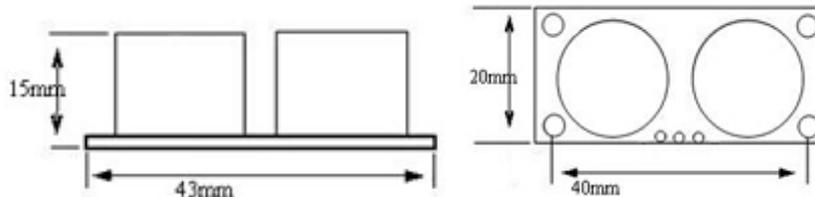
Dimensiones físicas de sensor ultrasónico HC-RS04.
